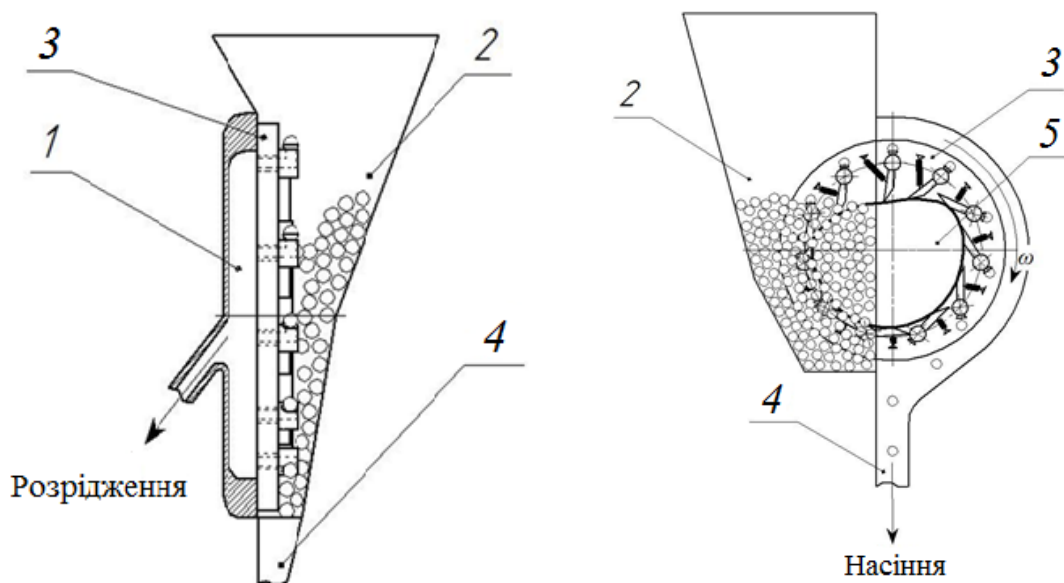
Пневмомеханічний висівний апарат з дозатором направленої дії: 1 – вакуумна камера; 2 – насіннева камера; 3 – висівний диск; 4 – насіннепровід; 5 – копір.
